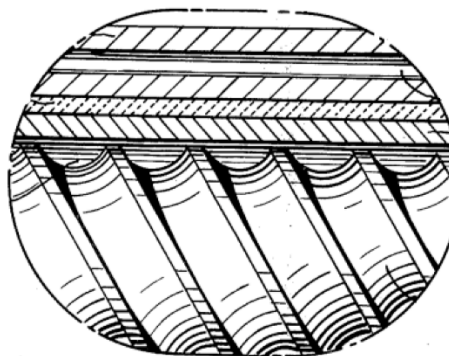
Футеровка в корпусі шнекового екструдера
